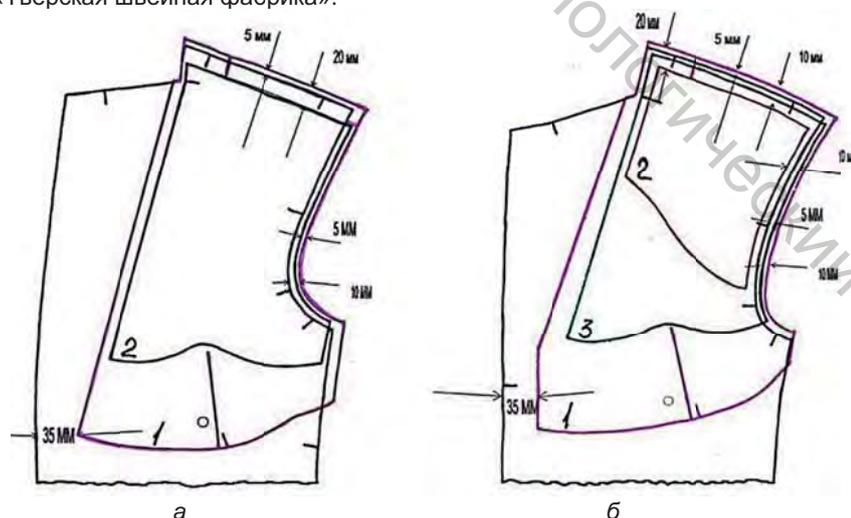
Схема сборки переда пиджака с БП: а – двухслойным; б – трехслойным
